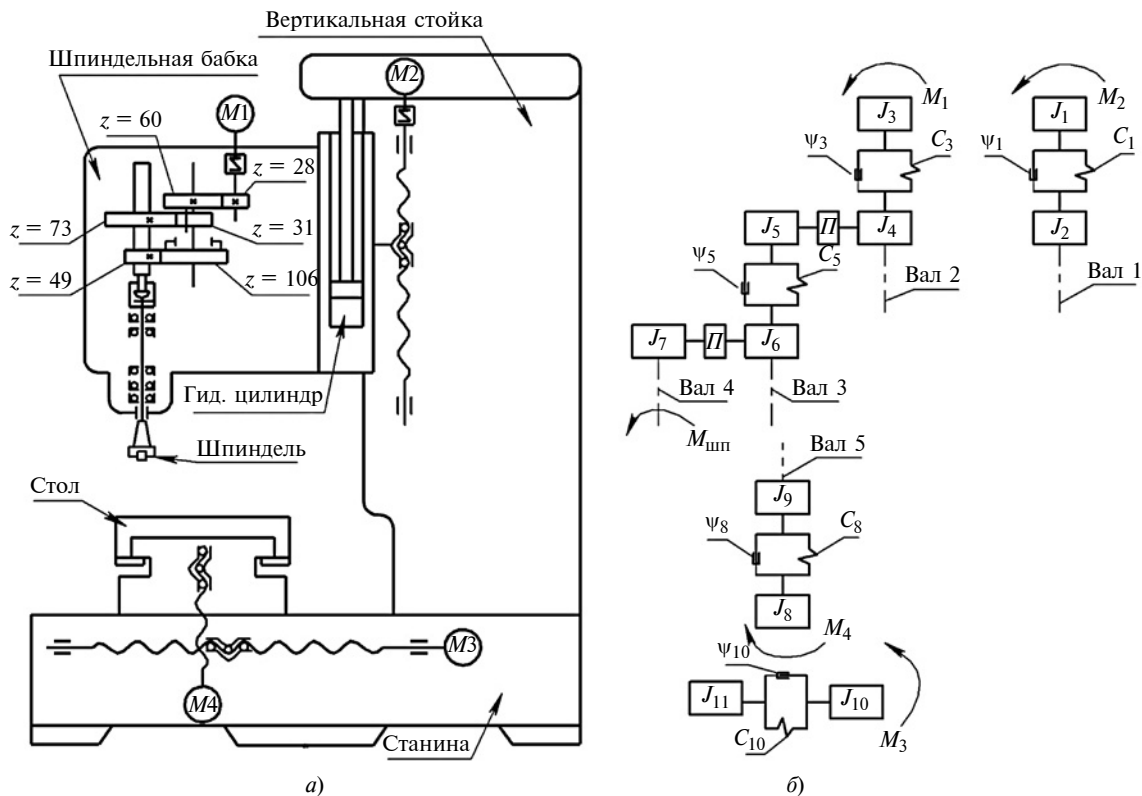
Кинематическая (а) и динамическая (б) схемы фрезерного станка с ЧПУ
